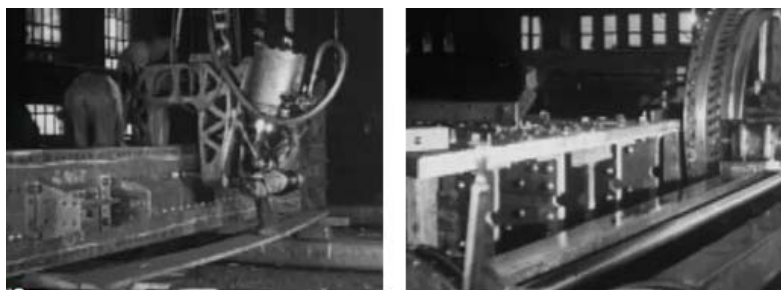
Изготовление колонн слева — клепка, справа — фрезеровка торцов
